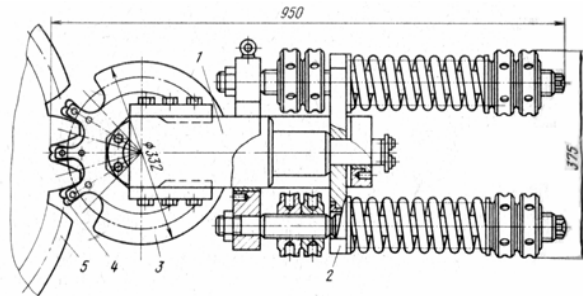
Устройство для поперечного обкатывания зубчатого колеса бортовой передачи экскаватора на токарном станке
